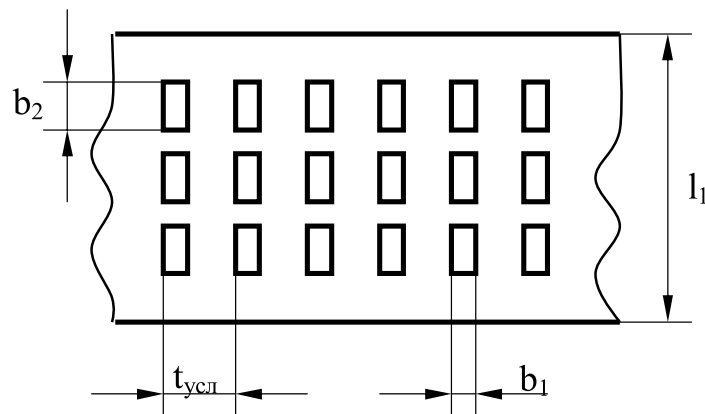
Развертка поверхности полого ротора ПЭМП
